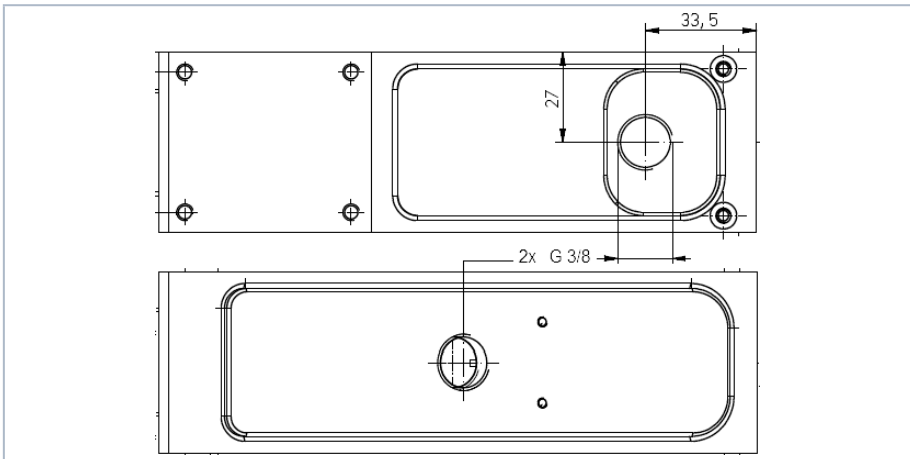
2 ELSA Steckverschraubungen (Push-In) in den Gewindebohrungen G 3/8 Zoll
